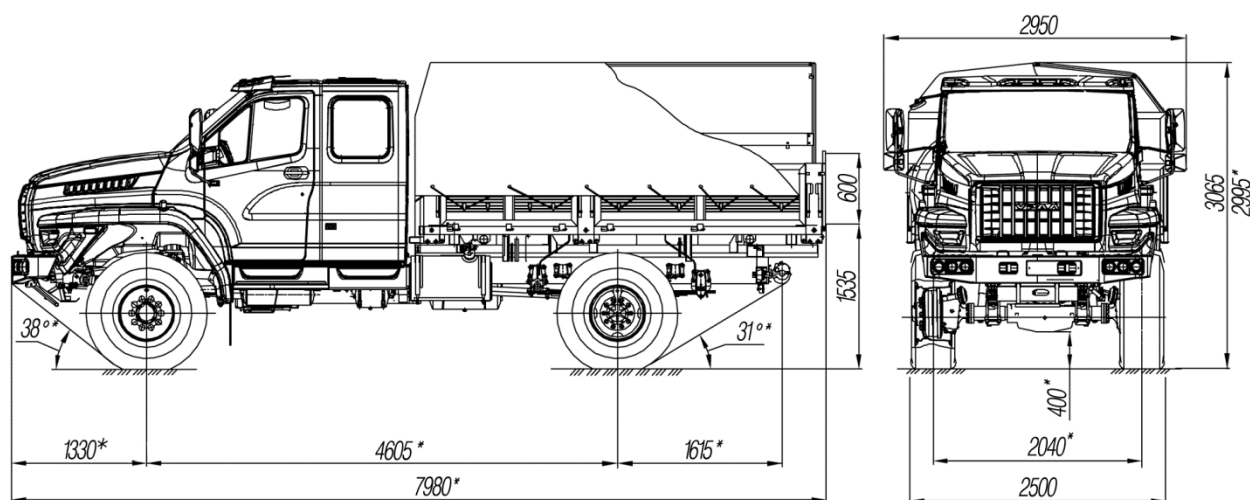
Габаритные размеры автомобиля Урал-43206-5551-71
